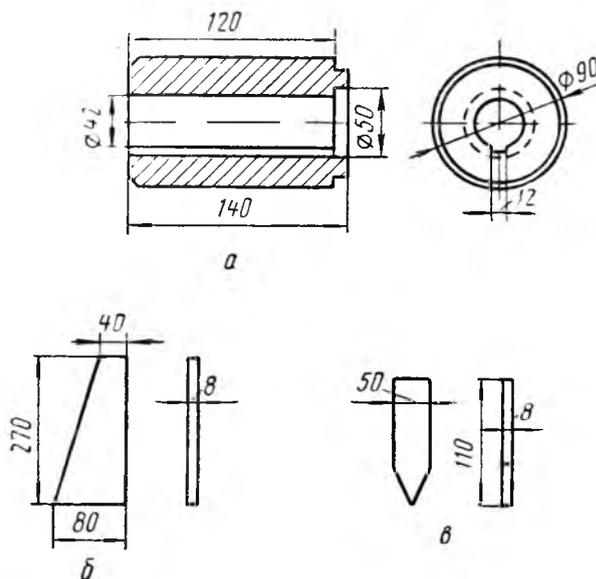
Основные детали приводных колес посадочного аппарата машины ЛМД-1 с тонким ободом: А — ступица колеса; Б — ребро жесткости; В — почвозащелка
